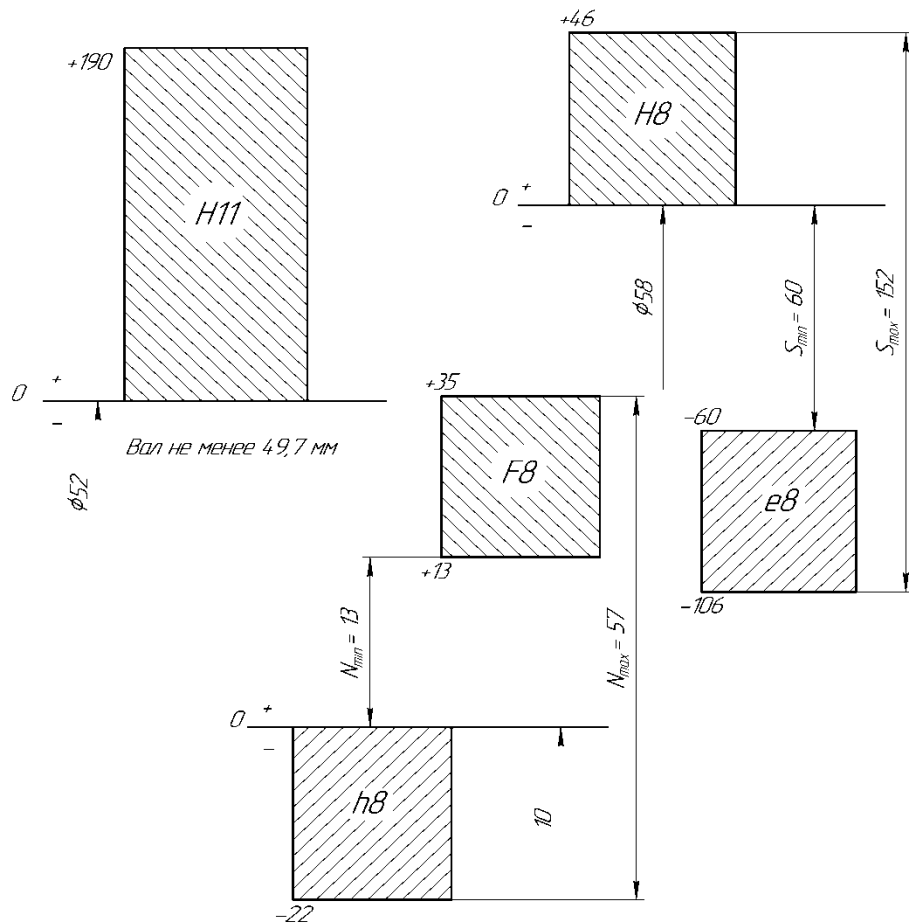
Схема полей допусков деталей шлицевого соединения
